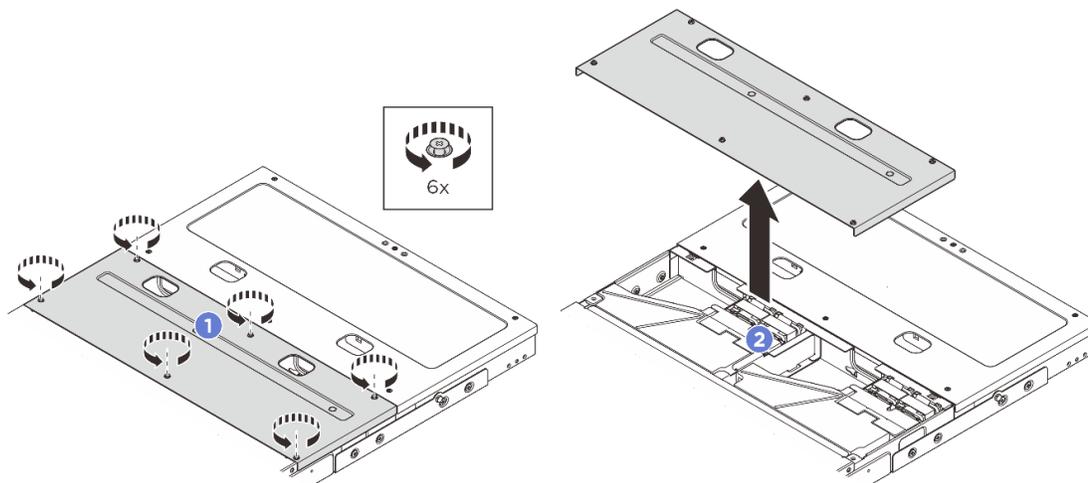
Снятие среднего верхнего кожуха корпуса 1U2N
